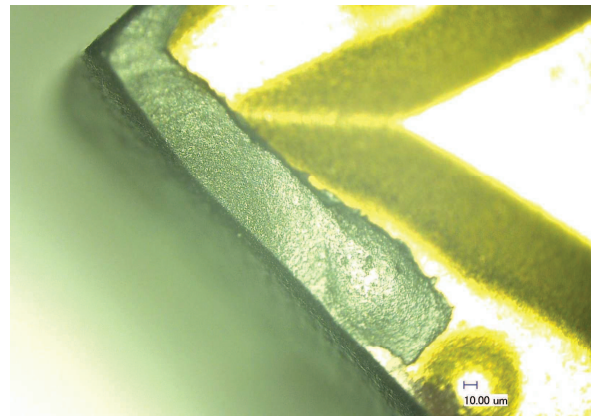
Ausbrüche in Richtung der Bohrachse entlang einer Schneidkante
